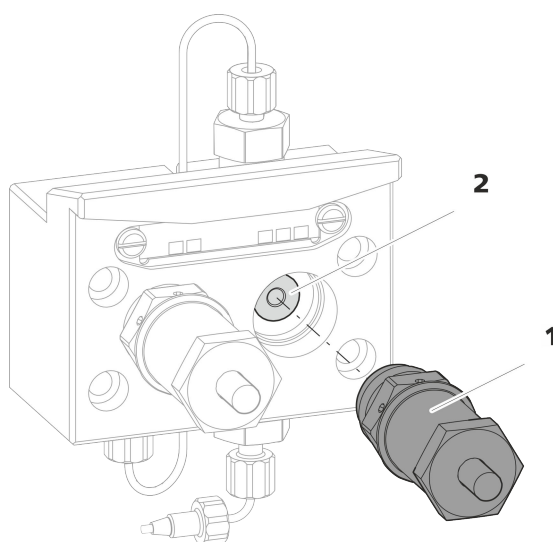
Desmontaje de cabezal de bomba – cartucho de pistón
